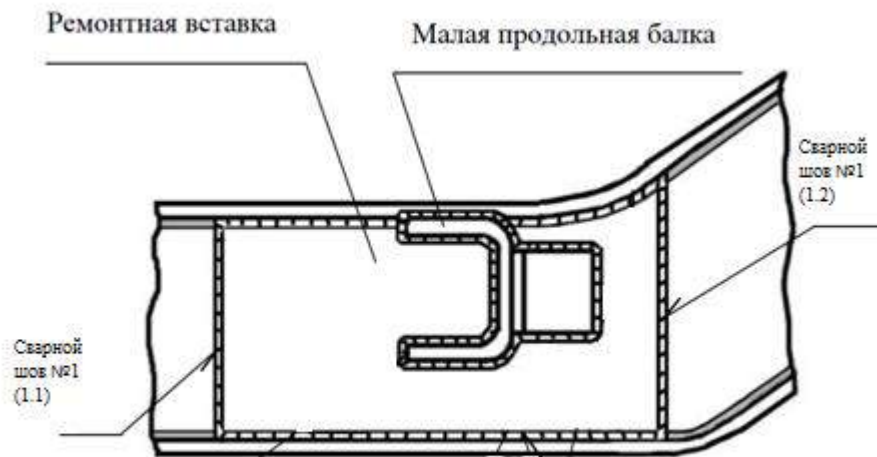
Эскиз сварных соединений ремонтной вставки с остающейся подкладкой (сварной шов №1)
